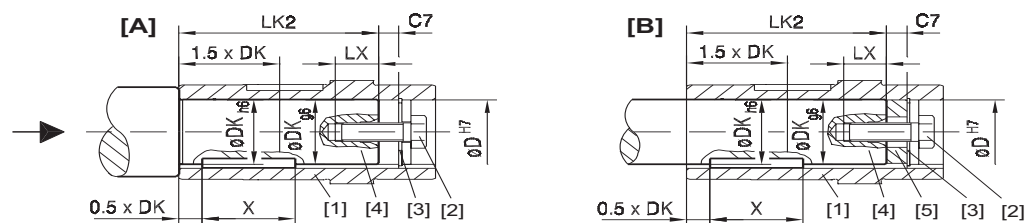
Ведомый вал с опорным выступом (A) и без опорного выступа (B)
